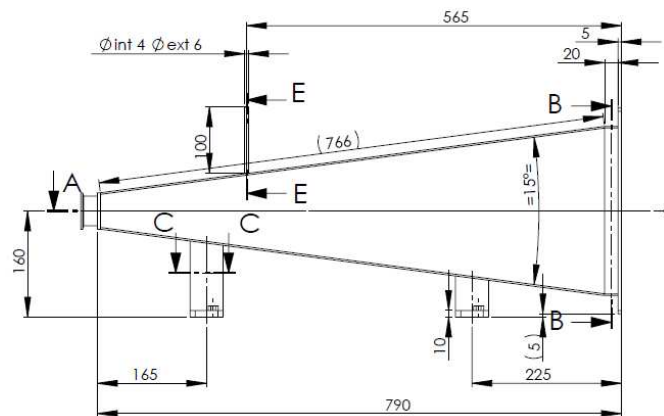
Plan du divergent à l'entrée de la section d'essais
